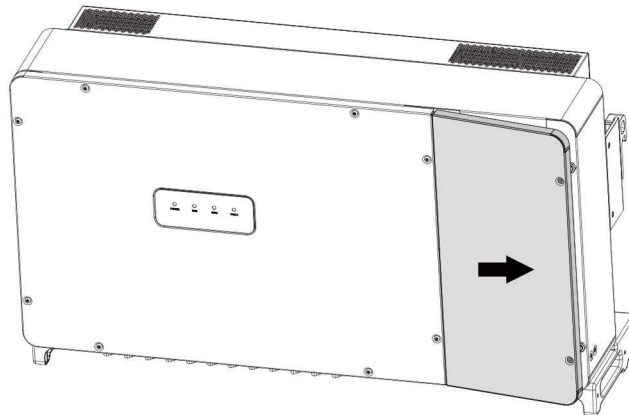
Cierre la cubierta superior de la caja de cables
